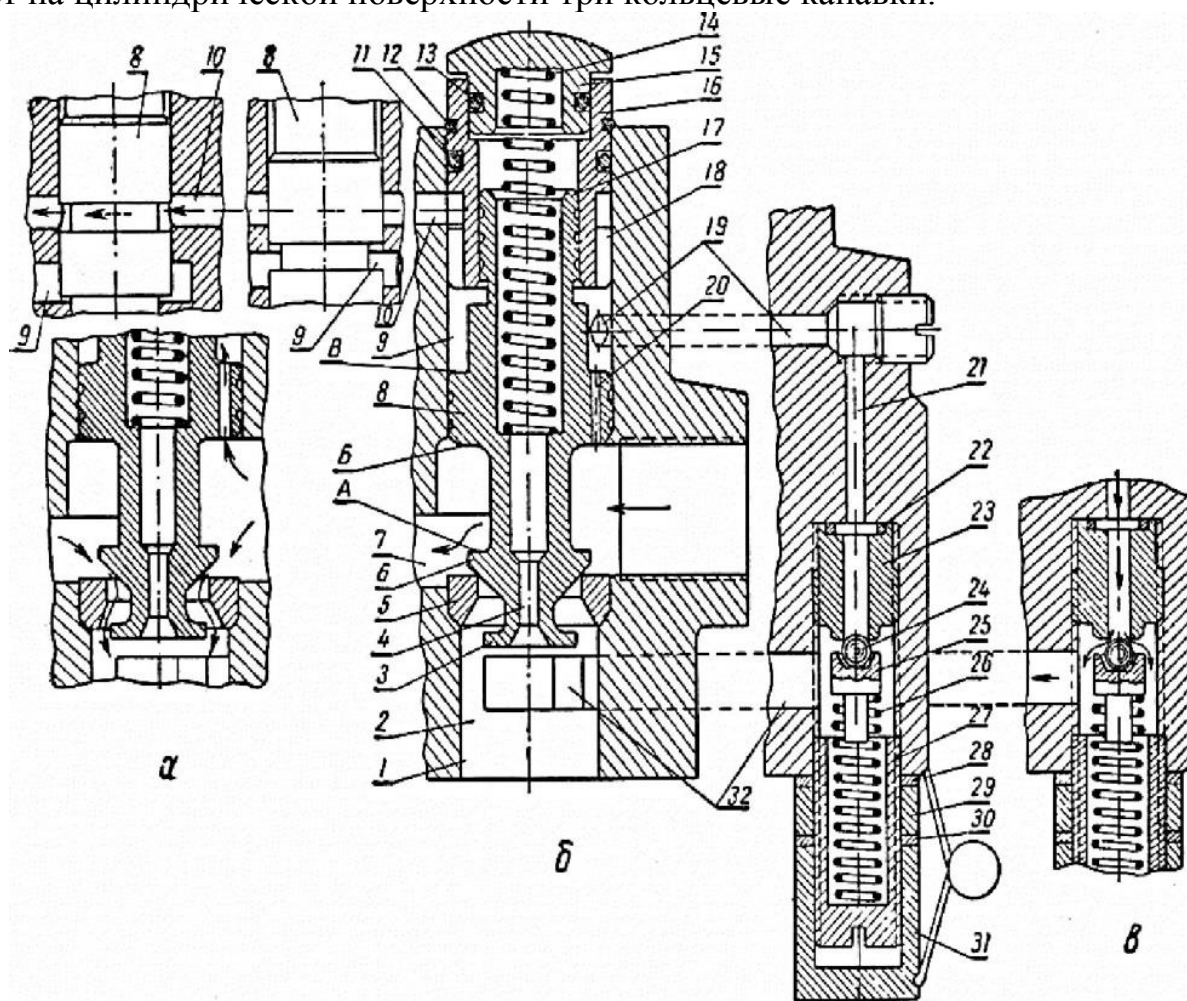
Перепускной и предохранительный клапаны:
